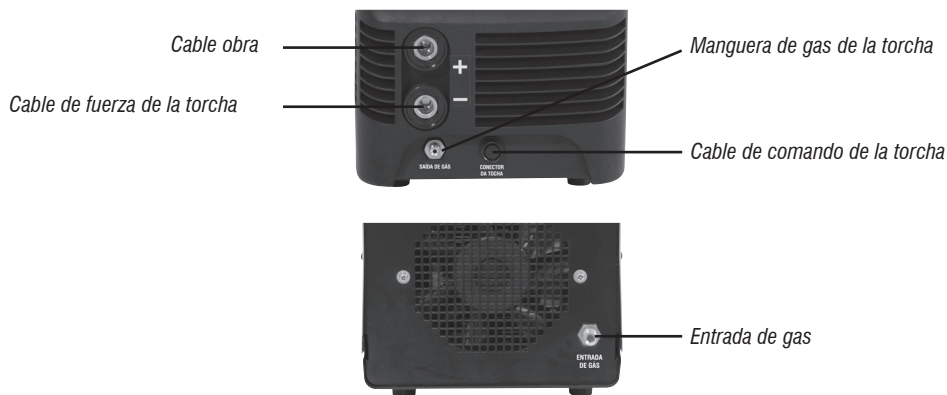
Sistema de conexión para soldadura TIG
